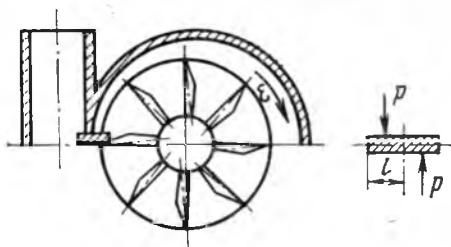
Схема крушения кусков коры между лопаткой и «языком» корпуса вентилятора
